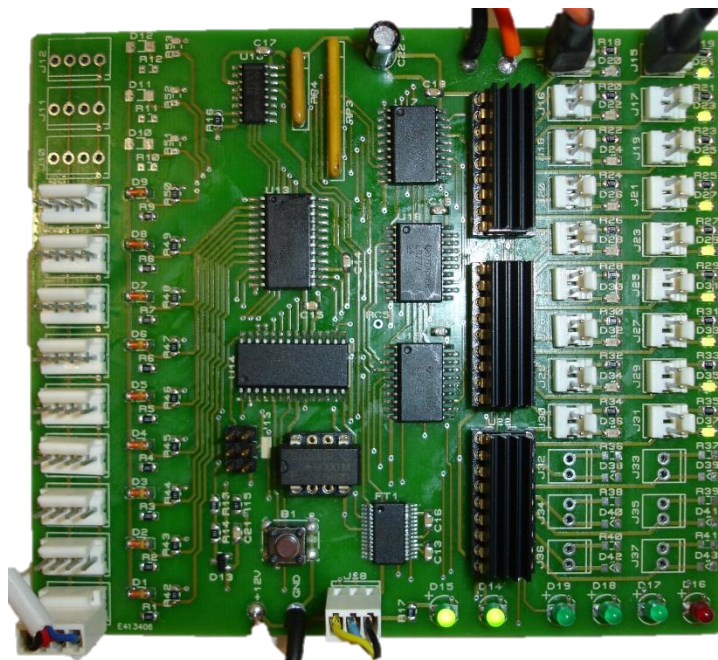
PCB após montagem de todos os componentes electrónicos.
